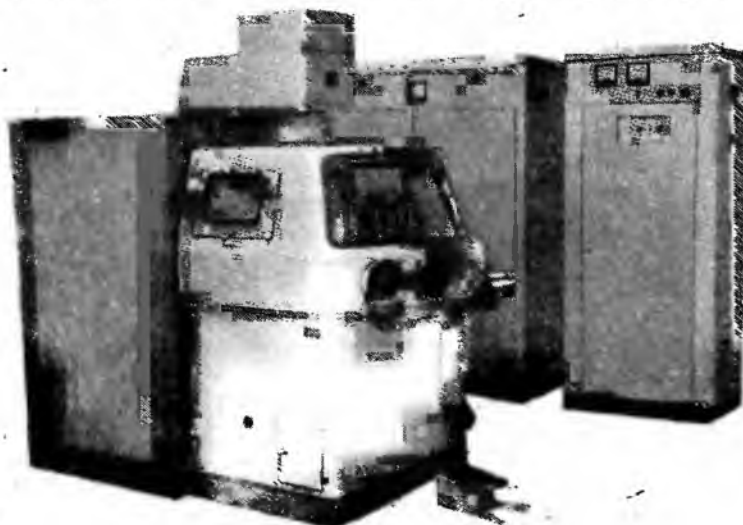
Машина МРК-10001 для рельефной конденсаторной сварки.
